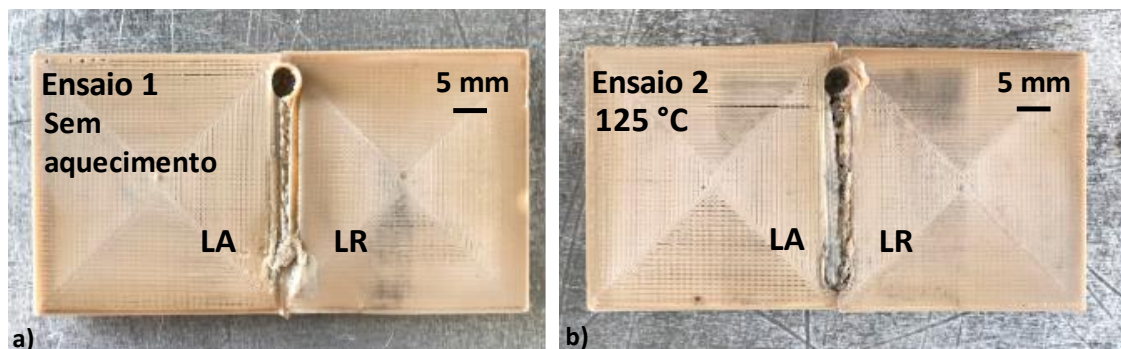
Aspeto visual da superfície das placas soldadas de PEEK: a) Ensaio 1, b) Ensaio 2.
